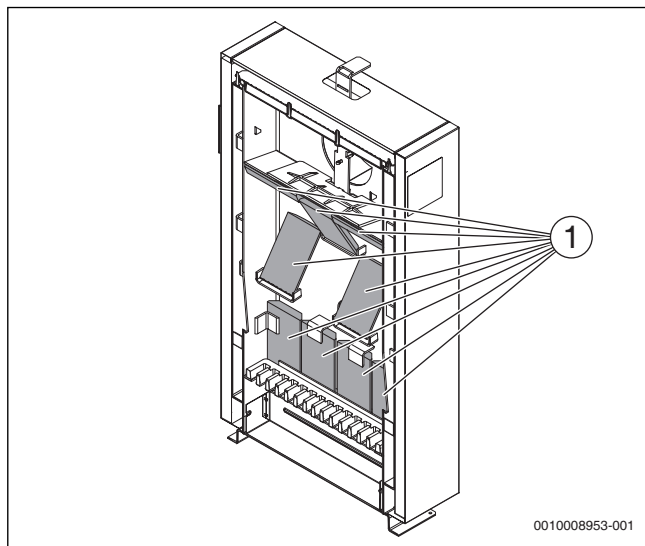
Lage der Feuerraumsteine im Feuerraum (Frontansicht)
